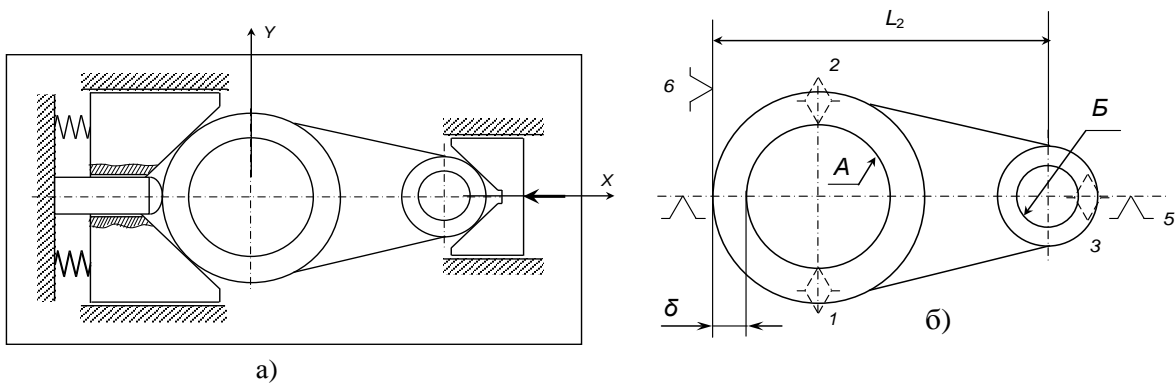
Конструктивна схема верстатного пристрою за варіантом 3 з установленою вихідною заготовкою (а) і відповідною схемою базування (б)
